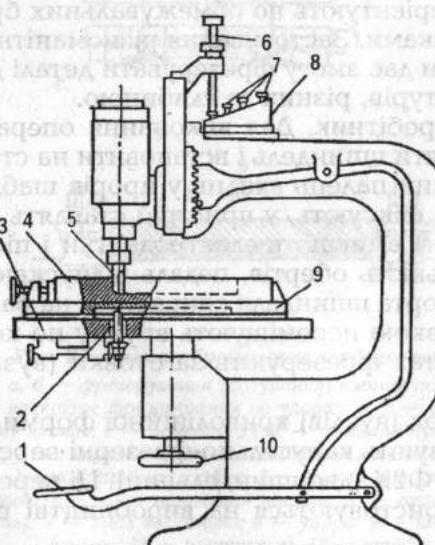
Одношпиндельний копіювальний верстат ВФК-1:
